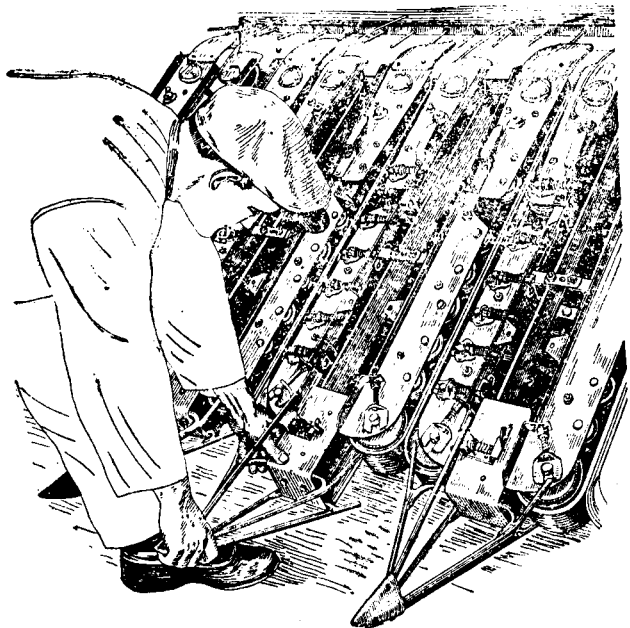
Постановка делителя и проверка действия отбрасывающей пружины.
